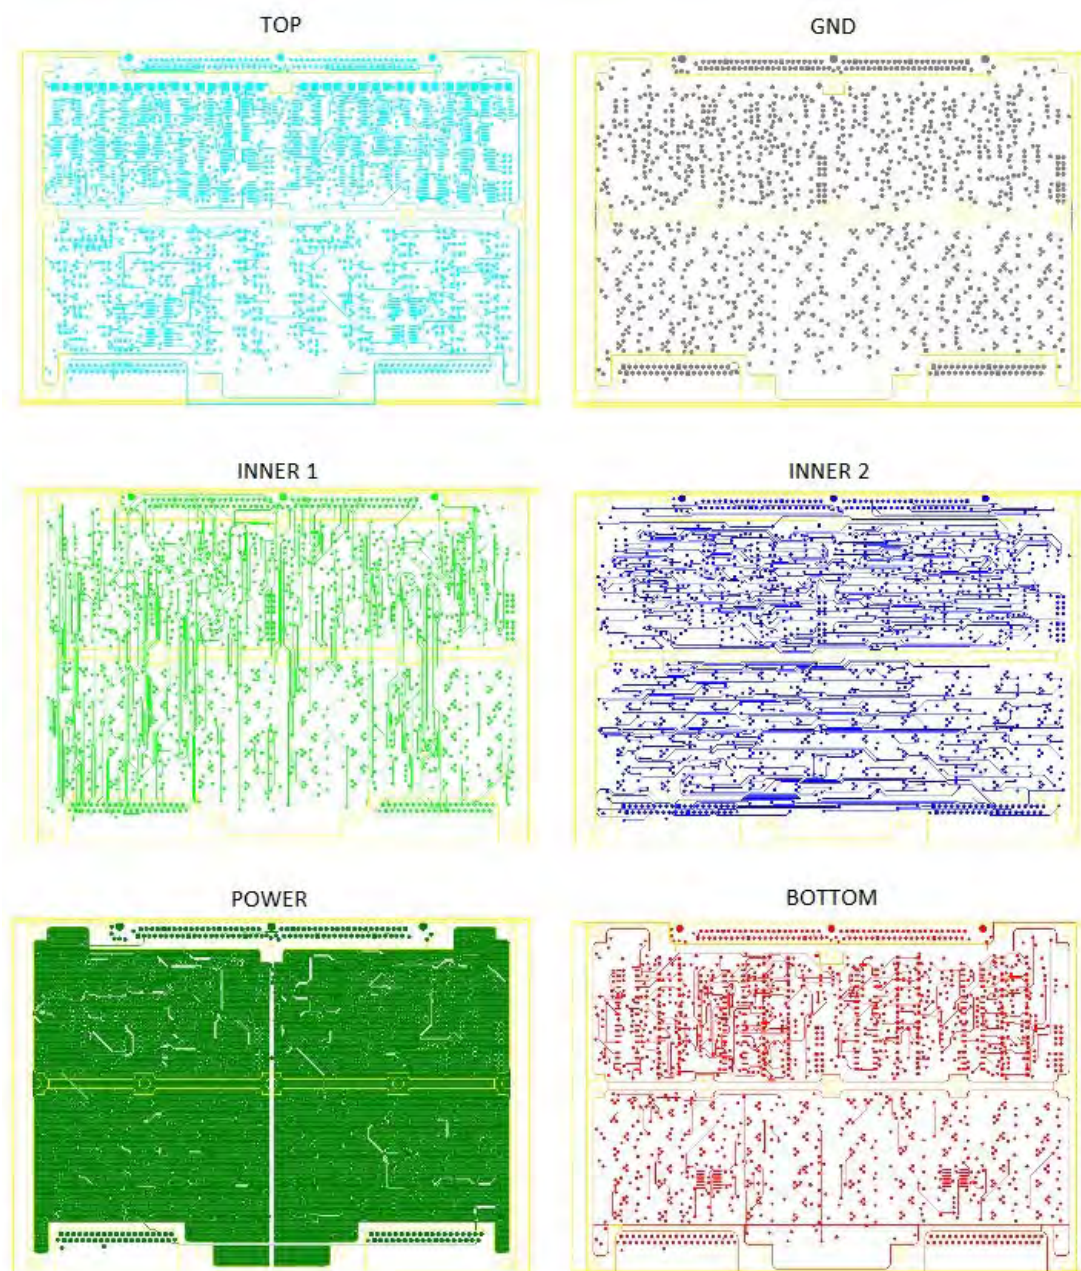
Desenho das camadas de cobre da PCB\_01.
